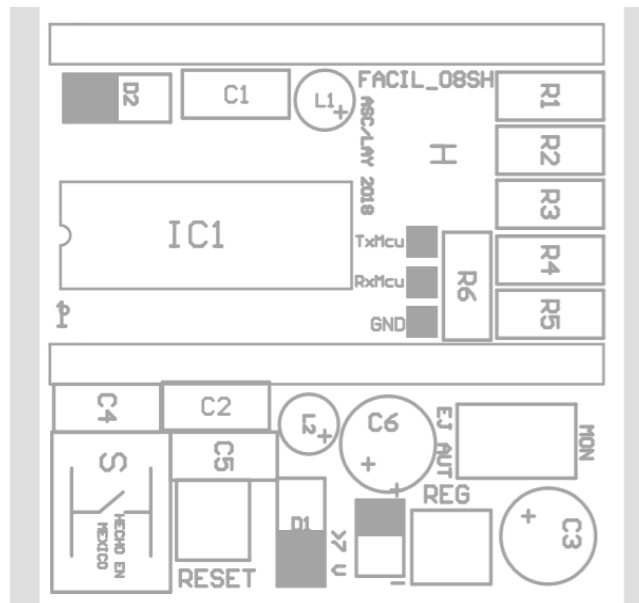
Respaldo de componentes en PCB de la tarjeta FACIL_08SH
